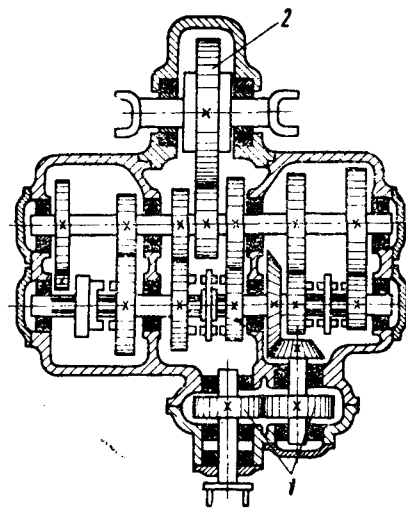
Схема пятиступенчатой коробки передач Д. Броун для спортивного автомобиля с передним расположением двигателя (главная передача условно повернута в плоскость чертежа).
